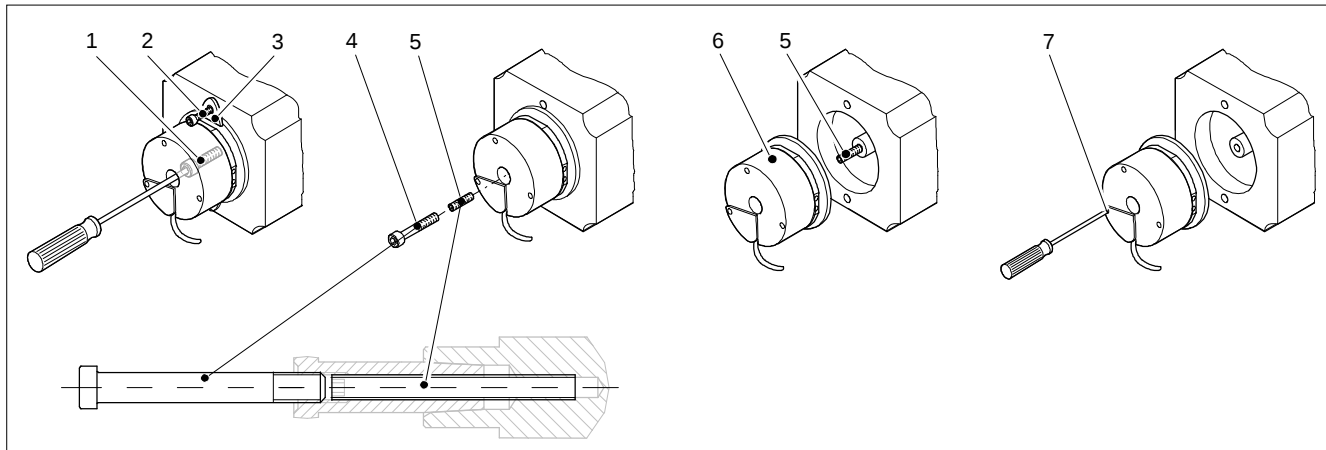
Abdrücken des Gebers mit Gewindestift und Schraube
